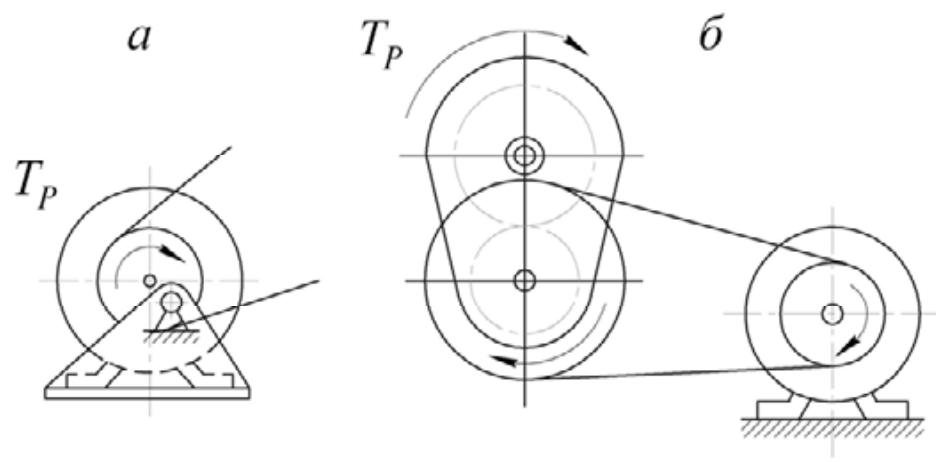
Способы автоматического натяжения ремня за счет реактивного момента: на корпусе электродвигателя (а); на корпусе редуктора (б)
